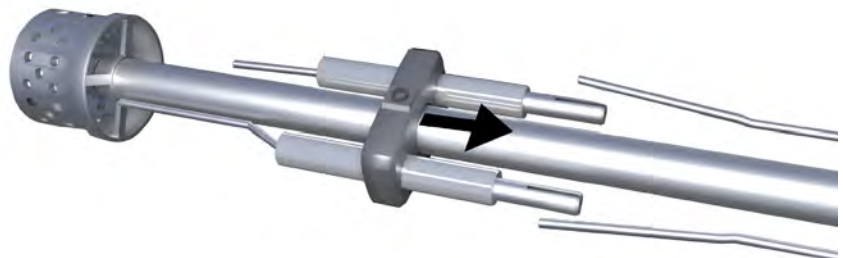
Etape 4 Remplacer les pièces d'usure du brûleur d'allumage
